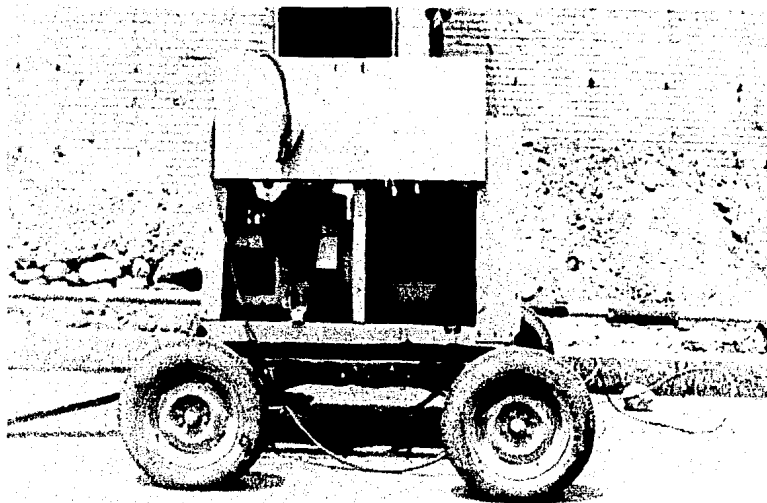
Soldadora con motor a Gasolina.
